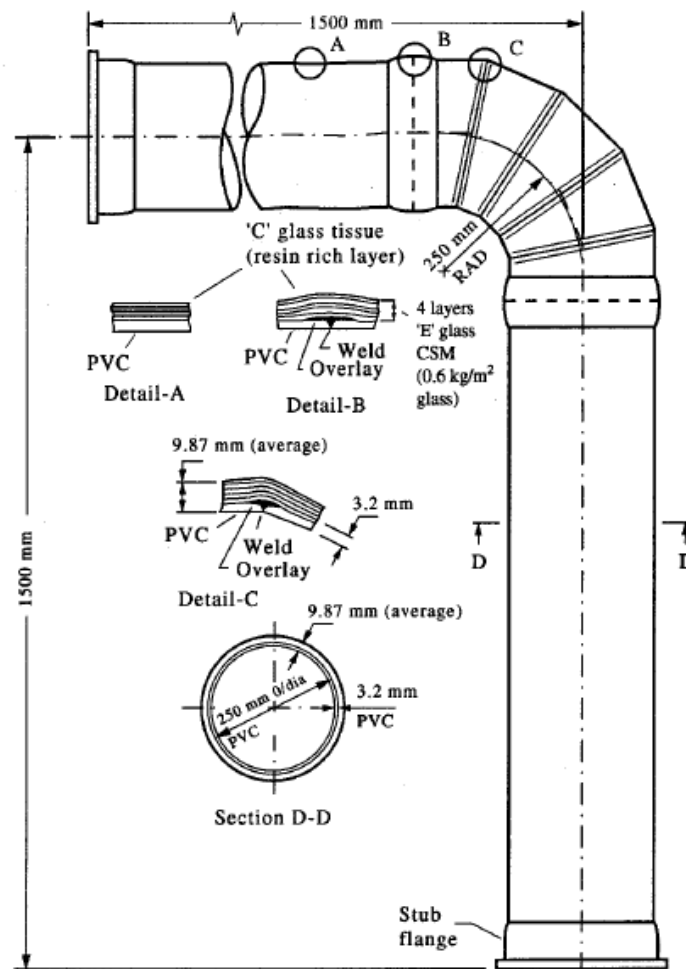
Conjunto construído para os testes de *Kitching e Hose* [26].
